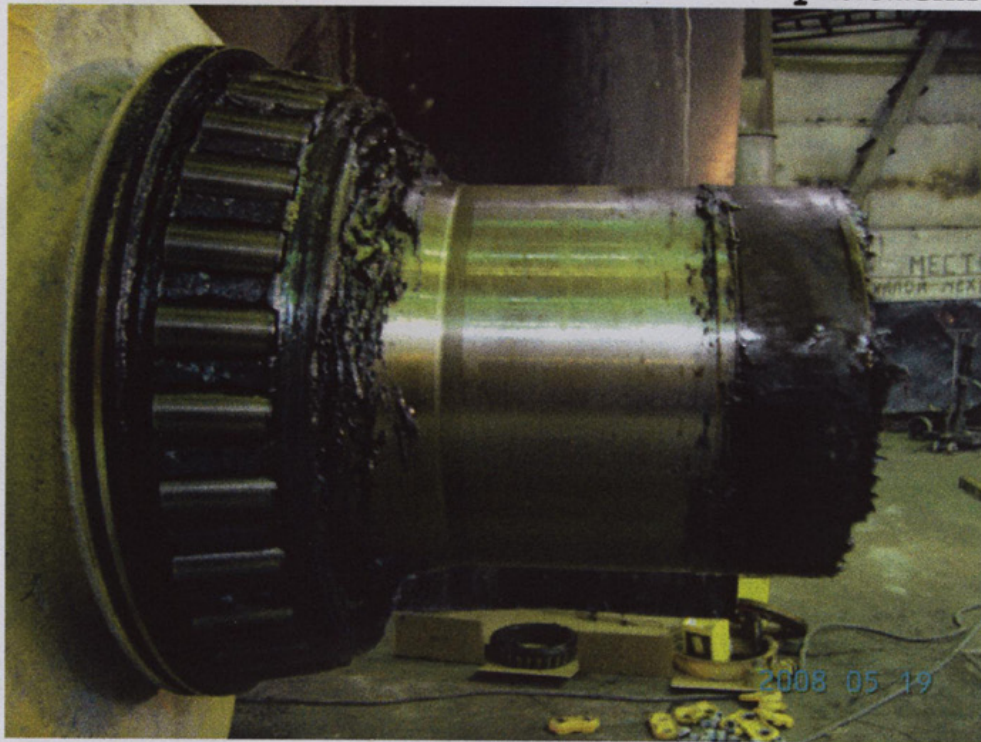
Вал после снятия крышки со смазкой МС-1000.
